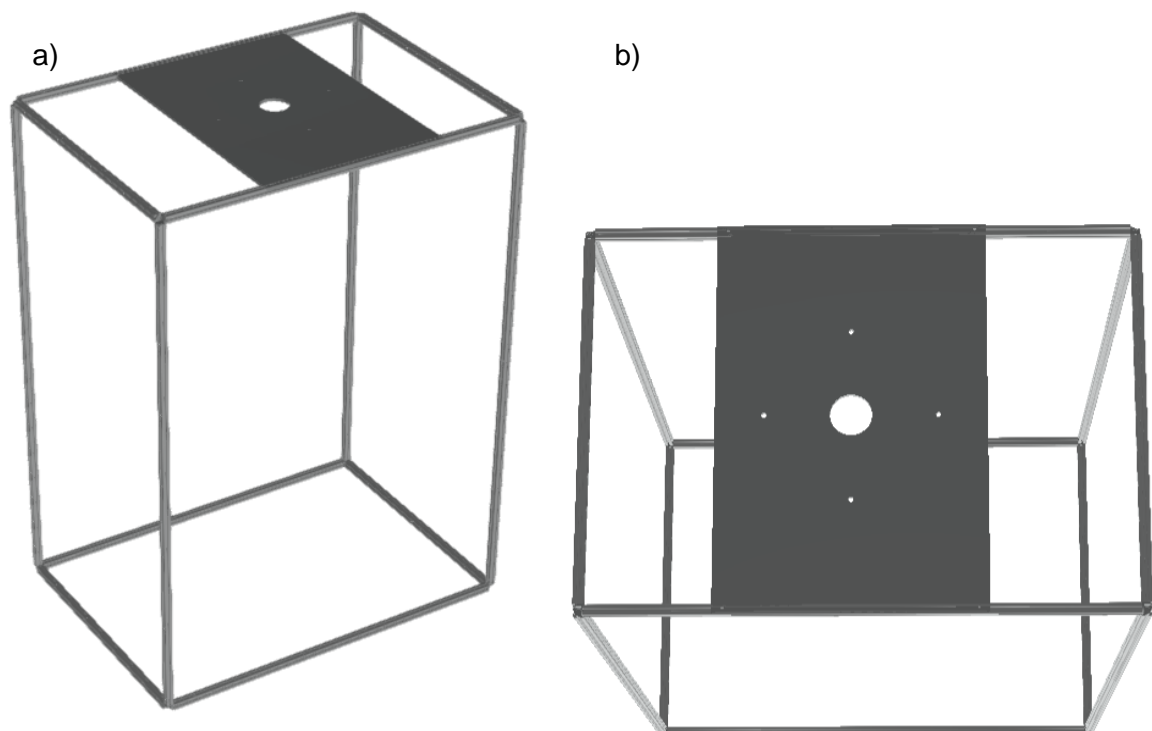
Modelo 3D de la estructura de soporte. (a) Vista de la estructura. (b) Vista de la plancha superior.
